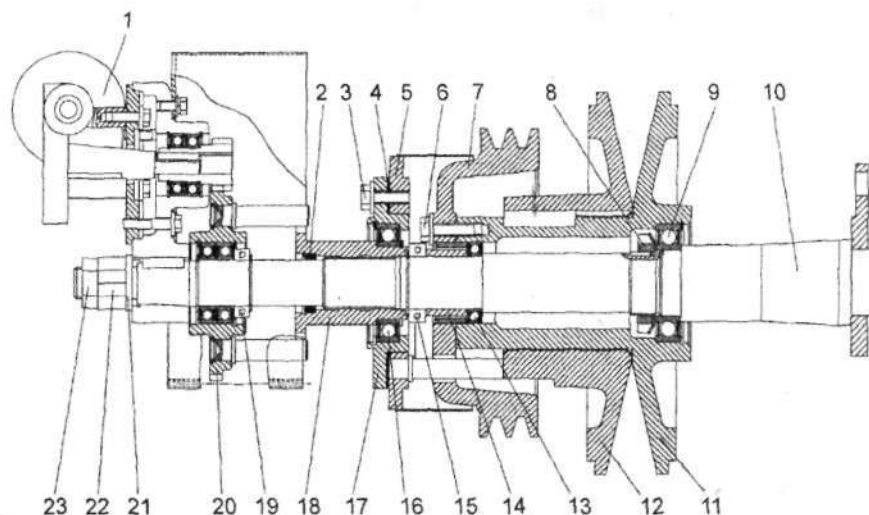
Контрпривод вариатора: 1 – привод; 2, 4 – прокладки; 3, 6 – болты; 5 – упор; 7, 11, 12 – шкивы; 8, 22, 23 – гайка; 9, 13, 15, 16, 19 – подшипники; 10 – ось; 14, 18 – втулки; 17 – корпус; 20 – колесо; 21 – шайба
